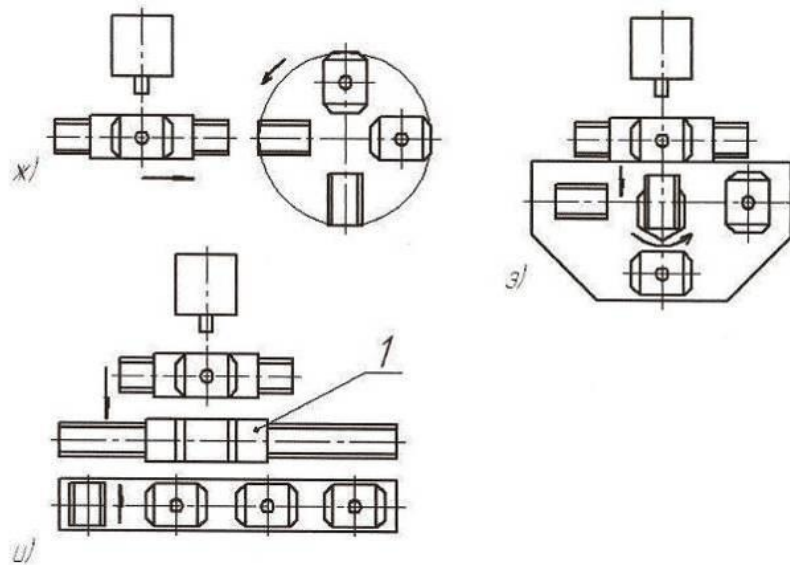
Компоновки багатопозиційних пристроїв:
